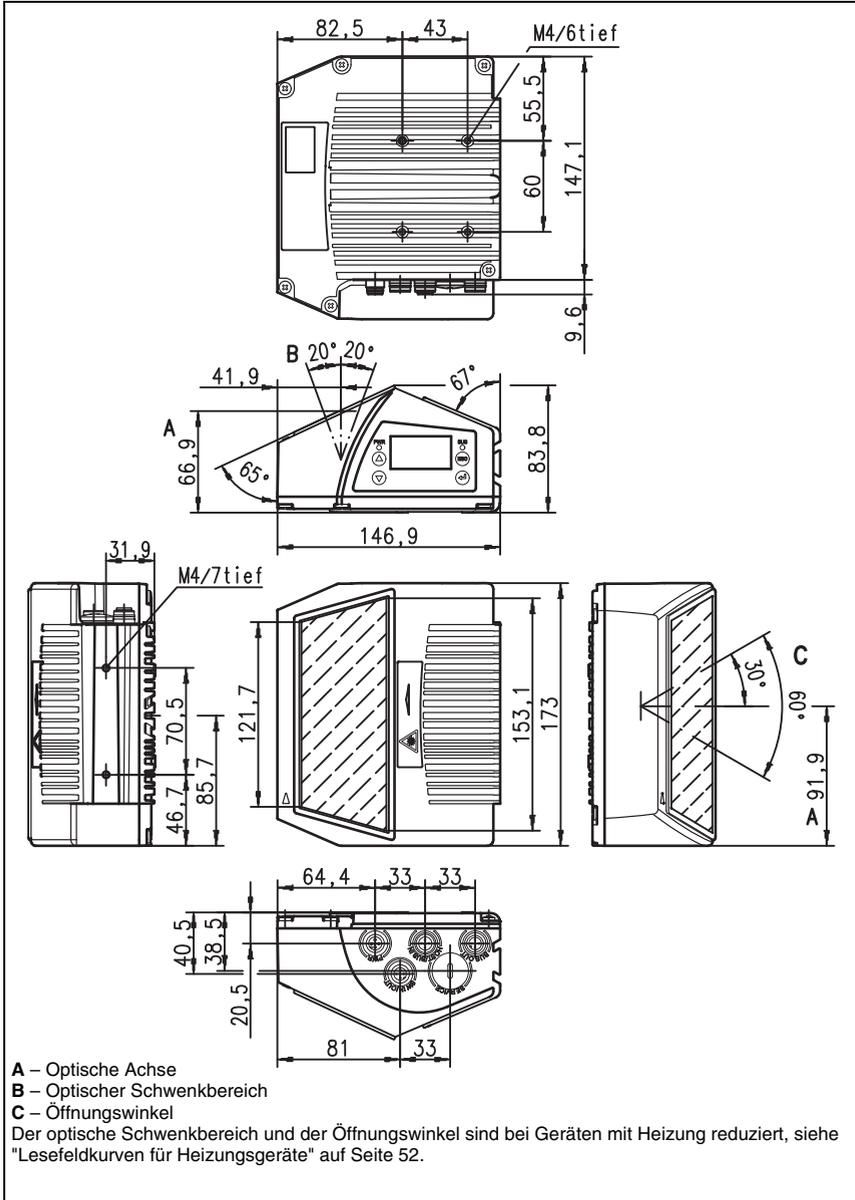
Maßzeichnung Scanner mit Schwenkspiegel BCL 504i O...100
